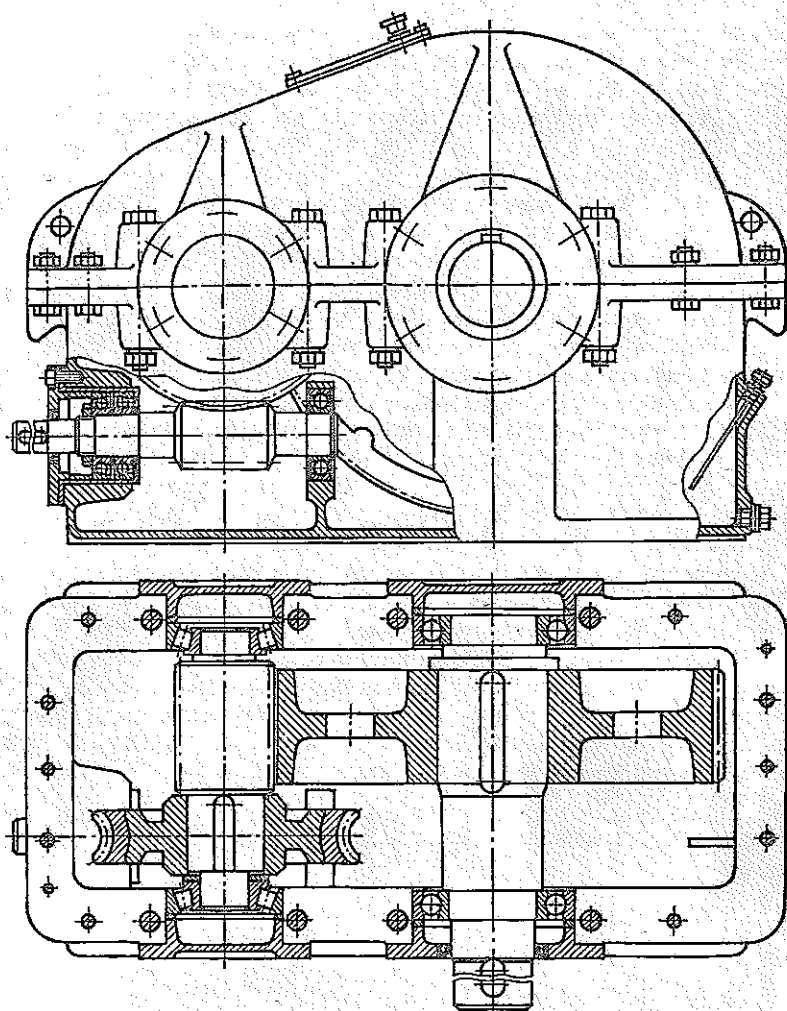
Червячно-цилиндрический двухступенчатый редуктор
